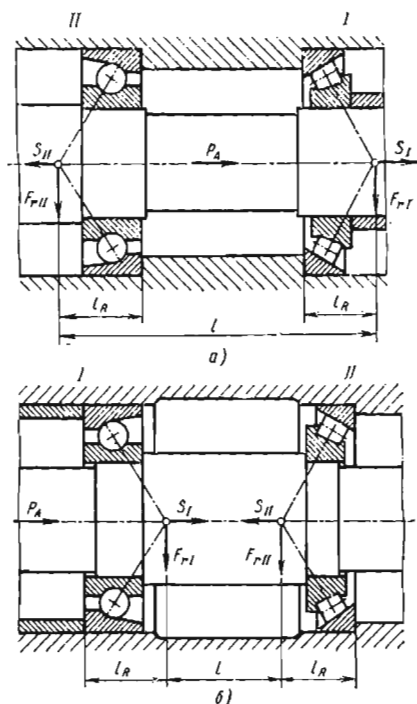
Схемы действия нагрузок при установке вала в радиально-упорных однорядных шариковых или роликовых подшипниках:
